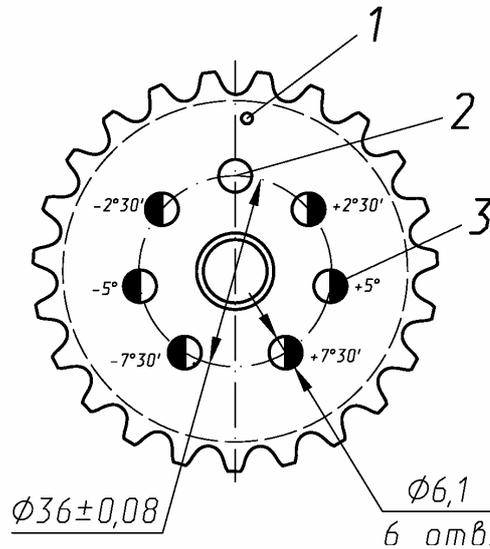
Звездочка распределительного вала с дополнительными отверстиями:
